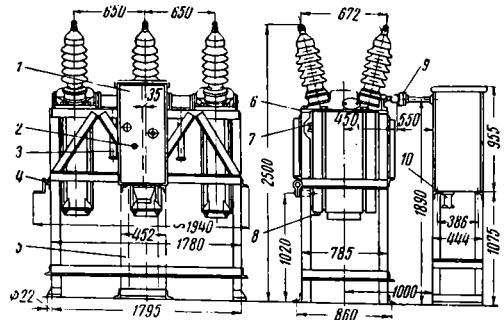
Выключатель типа ВМД-35: 1—шкаф с приводом; 2—кабельная муфта; 3—муфта шарнирная; 4—масловыпускной вентиль; 5—болт заземления; 6—ручное отключение; 7—указатель уровня масла; 8—лебедка с рукояткой; 9—газоотводная труба и аварийный клапан; 10—крышка; 11—бак;
